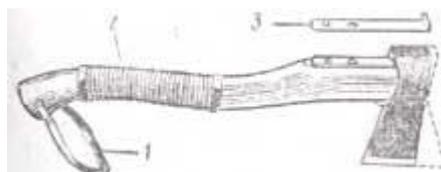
Крепление топора (7 — темляк; 3— обмотка шнуром; 3— металлическая пластина)
